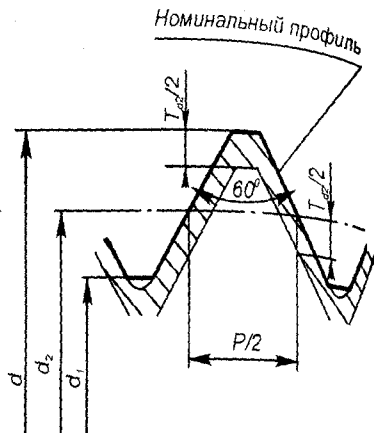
Схемы полей допусков наружной резьбы:
